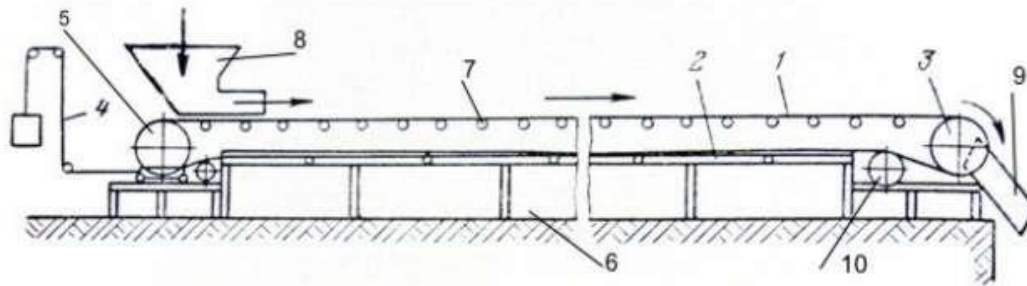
Типова схема обладнання стрічкового конвеєра: 1 – стрічка конвеєра, 2 – роликівий став, 3 – приводний барабан, 4 – натяжний пристрій, 5 – натяжний барабан, 6 – конвеєрний став, 7 – ролики з роликооперами робочої гілки, 8 – завантажувальний пристрій, 9 – розвантажувальний пристрій, 10 – відхиляючий барабан
